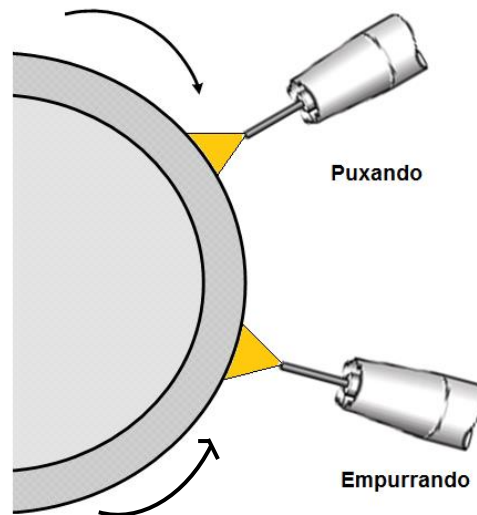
Técnica de soldagem puxando y empurrando na seção vertical descendente do tubo.
